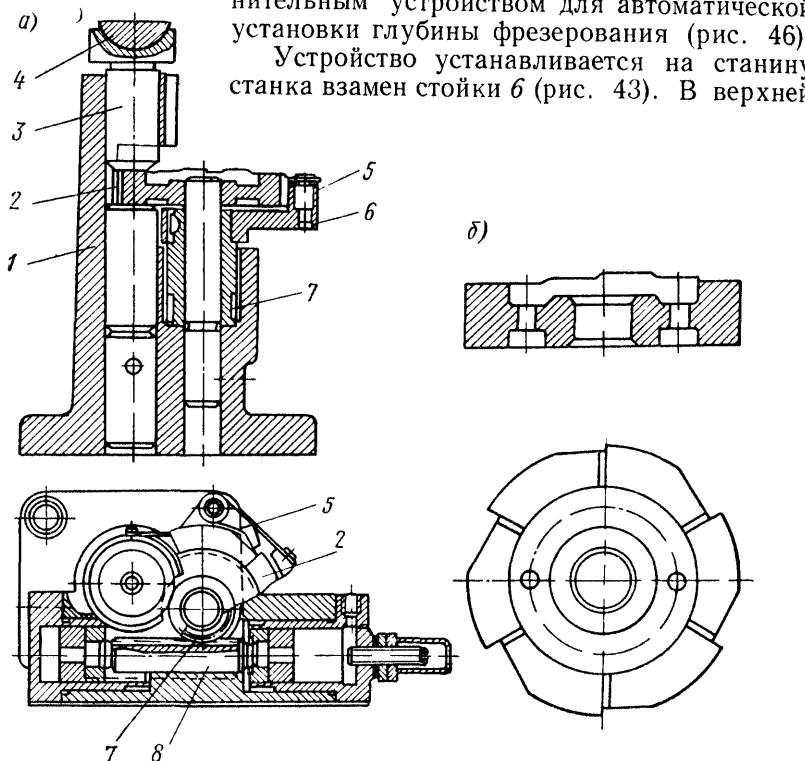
Механизм для автоматической установки глубины фрезерования на полуавтомате модели 6В2 (а) и диск установки глубины фрезерования (б)
